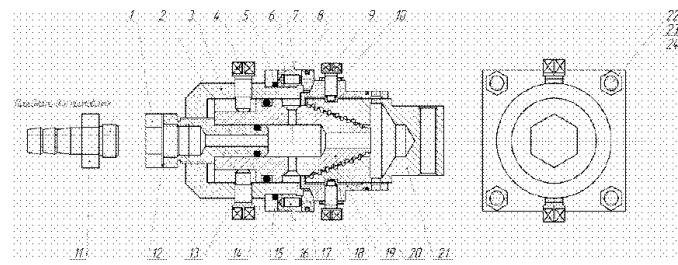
Конічний підшипник ковзання, здатний до самоочищення
